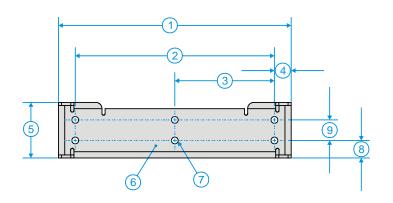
Befestigung des unteren Montagewinkels am Fahrzeug
